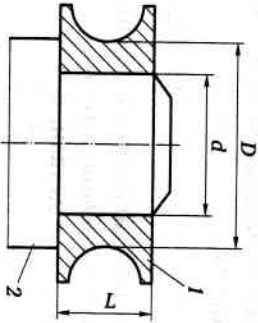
Схема напрессовки внутреннего кольца 1 подшипника на цапфу вала 2
